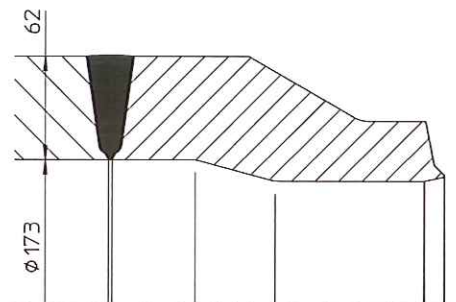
Schweißendenkonstruktion alter Baureihe für Einsitzregelventile
